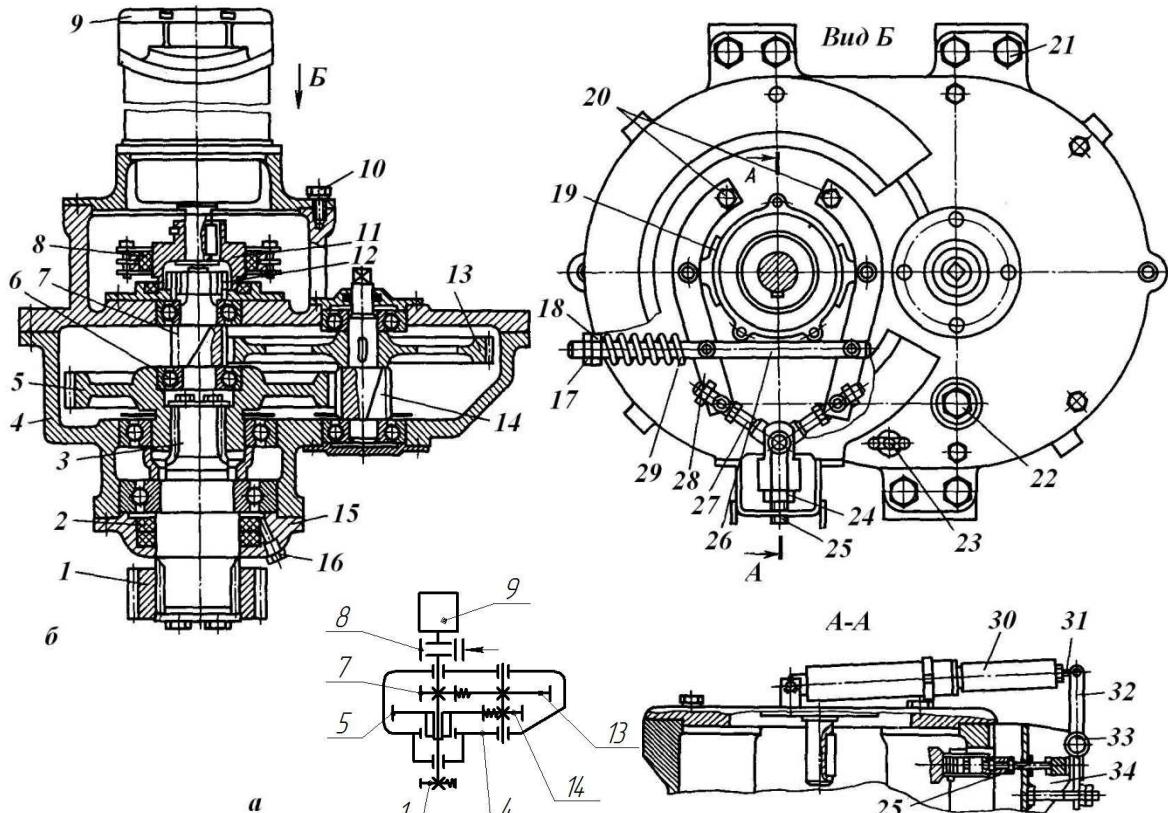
Механизм поворота крана КС-23571: *a* – кинематическая схема, *б* – общий вид; 1, 5, 13 – шестерни, 2 - сальник, 3 – выходной вал, 4 – редуктор, 6 – подшипник, 7, 14 – валы-шестерни, 8 – тормоз, 9 – гидродвигатель, 10, 21 – болты, 11 – шкив, 12 – зубчатая муфта, 15 – крышка, 16, 22 – сливная и заливная пробки, 17 – контргайка, 18, 24 – гайки, 19 – колодка, 20, 33 – оси, 23 – маслоуказатель, 25 – шток тормоза, 26, 27 – тяги, 29 – пружина, 30 – гидроразмыкатель, 31 – шток гидроразмыкателя, 34 - кронштейн
